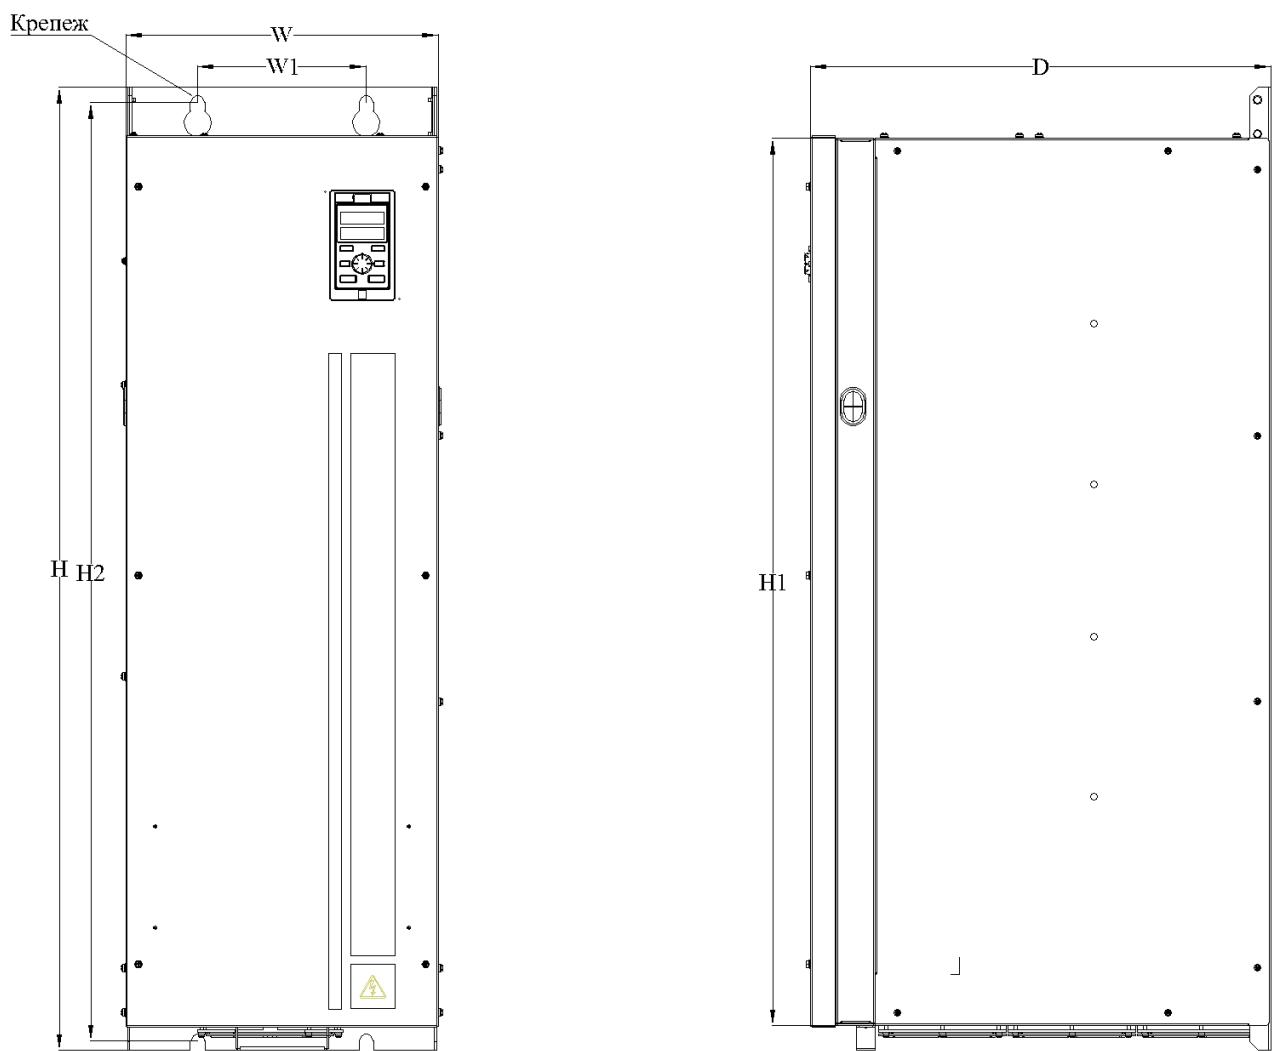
Чертеж преобразователя частоты типоразмер 9
